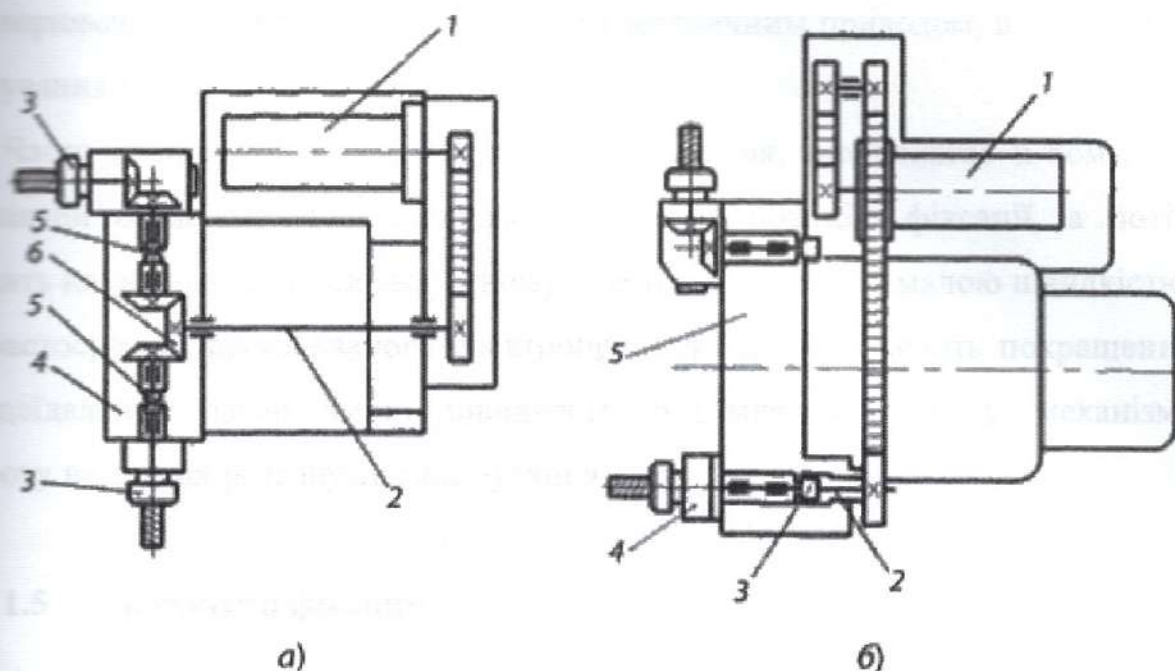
Приклади конструктивних схем обертання інструментів у револьверних головках: а - через конічні зубчасті передачі та сполучні муфти; б - через пасову передачу.
